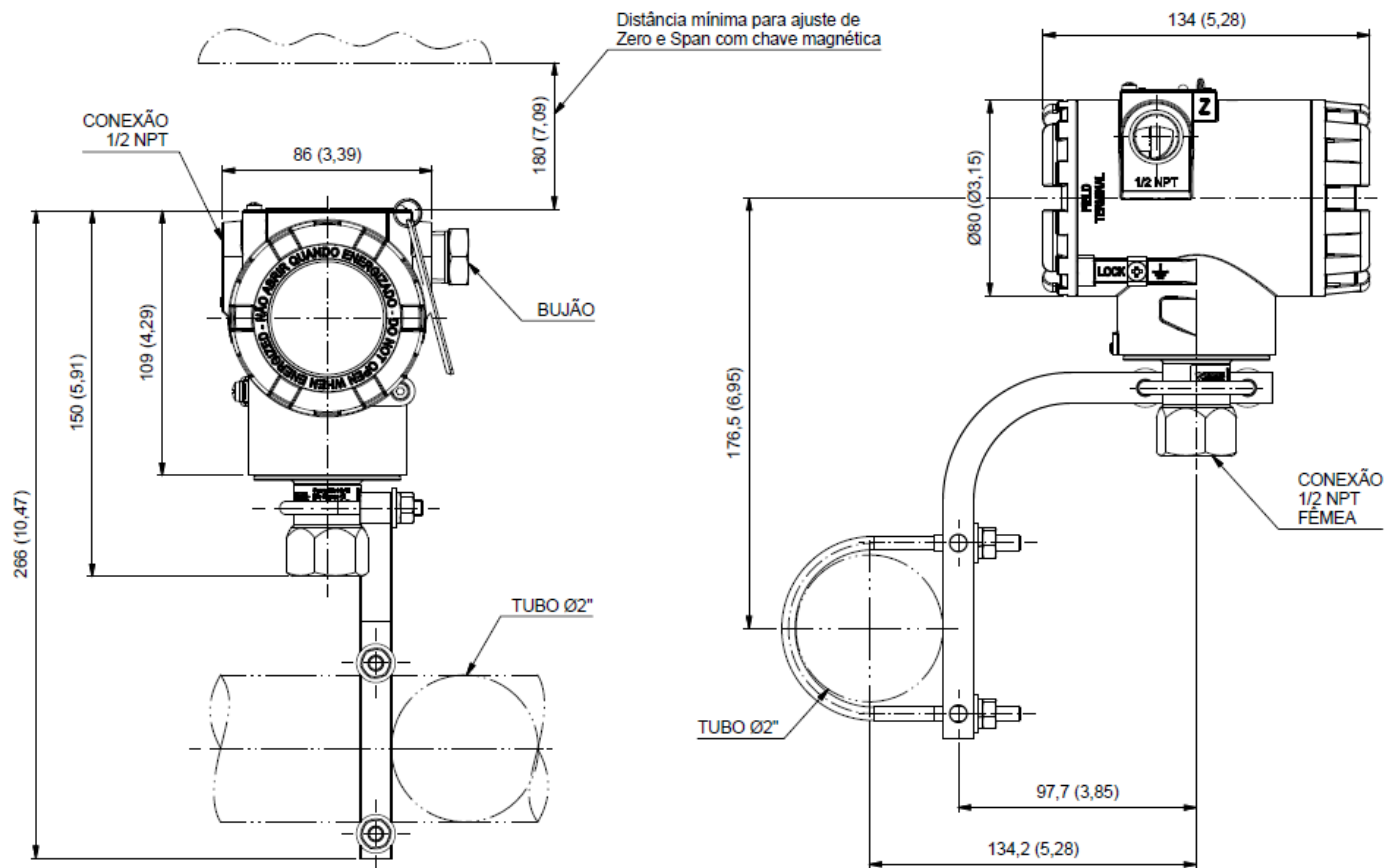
Desenho dimensional e esquema de montagem do VPT11 HART.
